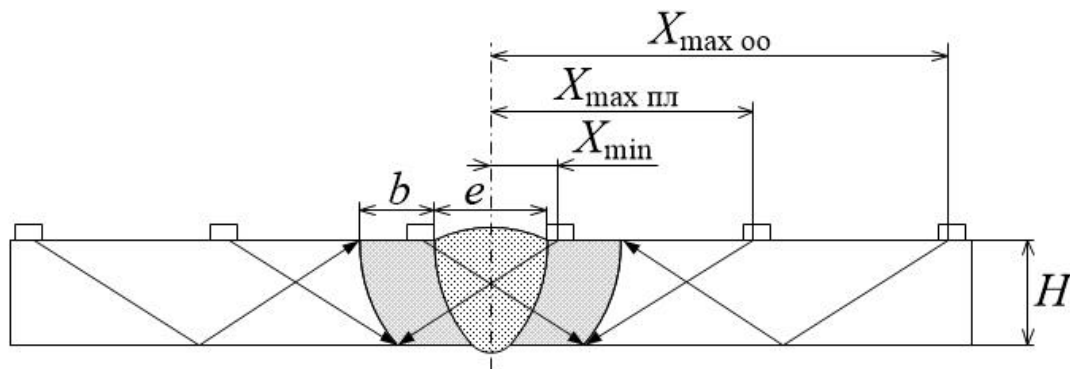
Схема контроля стыкового сварного соединения.
